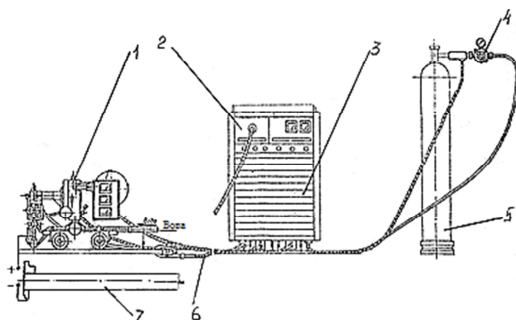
Схема установки АДГ-602 для автоматической электродуговой наплавки в среде углекислого газа (смеси защитных газов:
